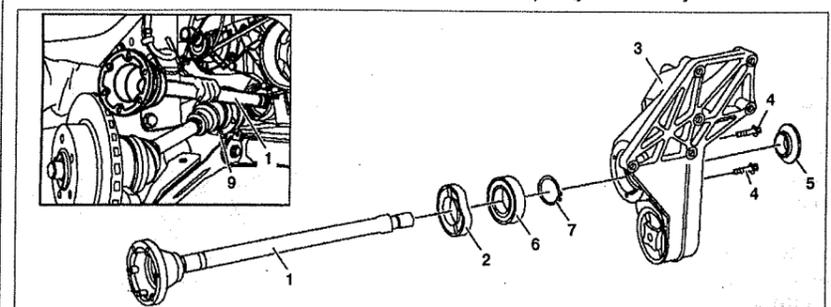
Центральный ведущий вал с подшипником (автомобили с двигателями 611.980): 1. Центральный ведущий вал, 2. Крышка подшипника, 3. Кронштейн, 4. Болт, 5. Пластическое защитное кольцо, 6. Подшипник, 7. Стопорное кольцо, 9. Полуось.
